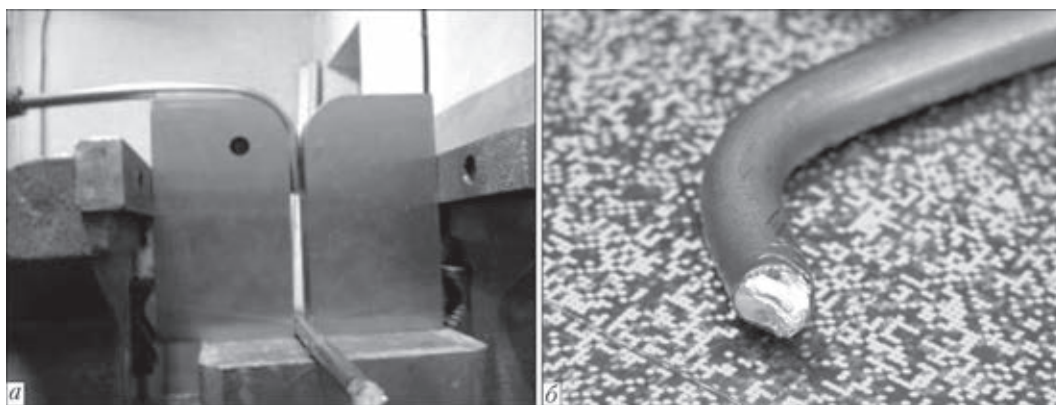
Общий вид способа испытаний на загиб (а) и вид излома прутка (б)
